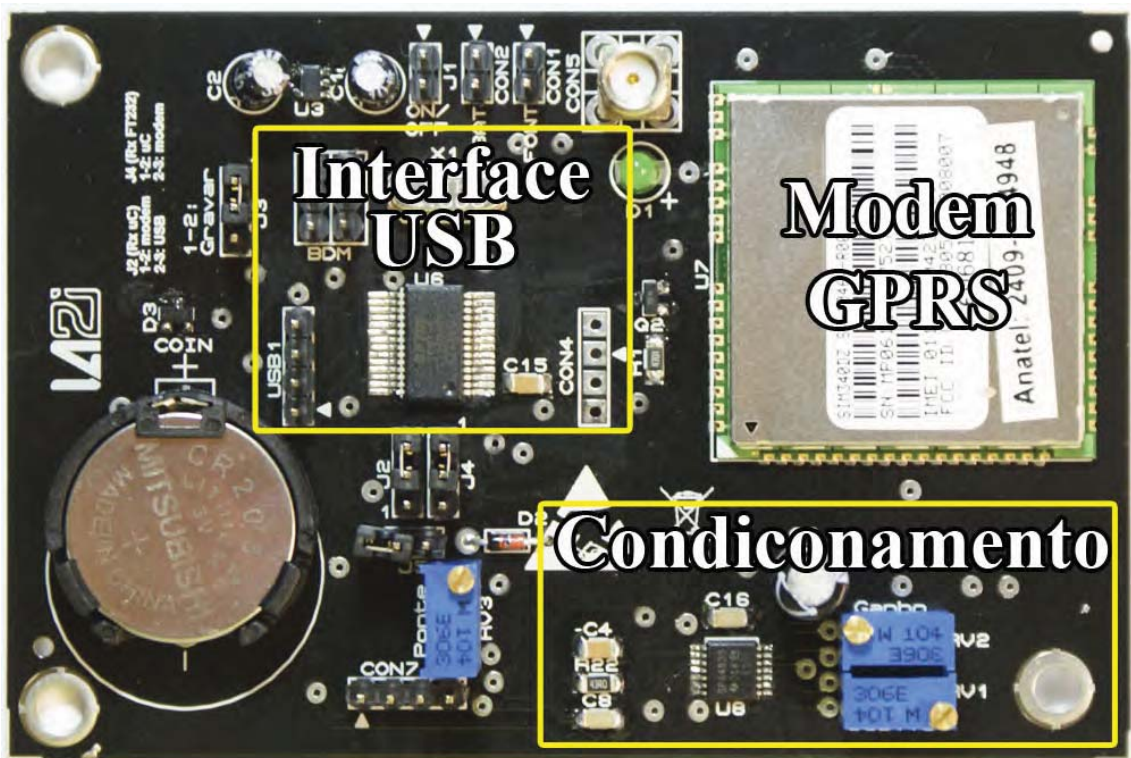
PCB - Lado dos Componentes. Foto: o autor.
